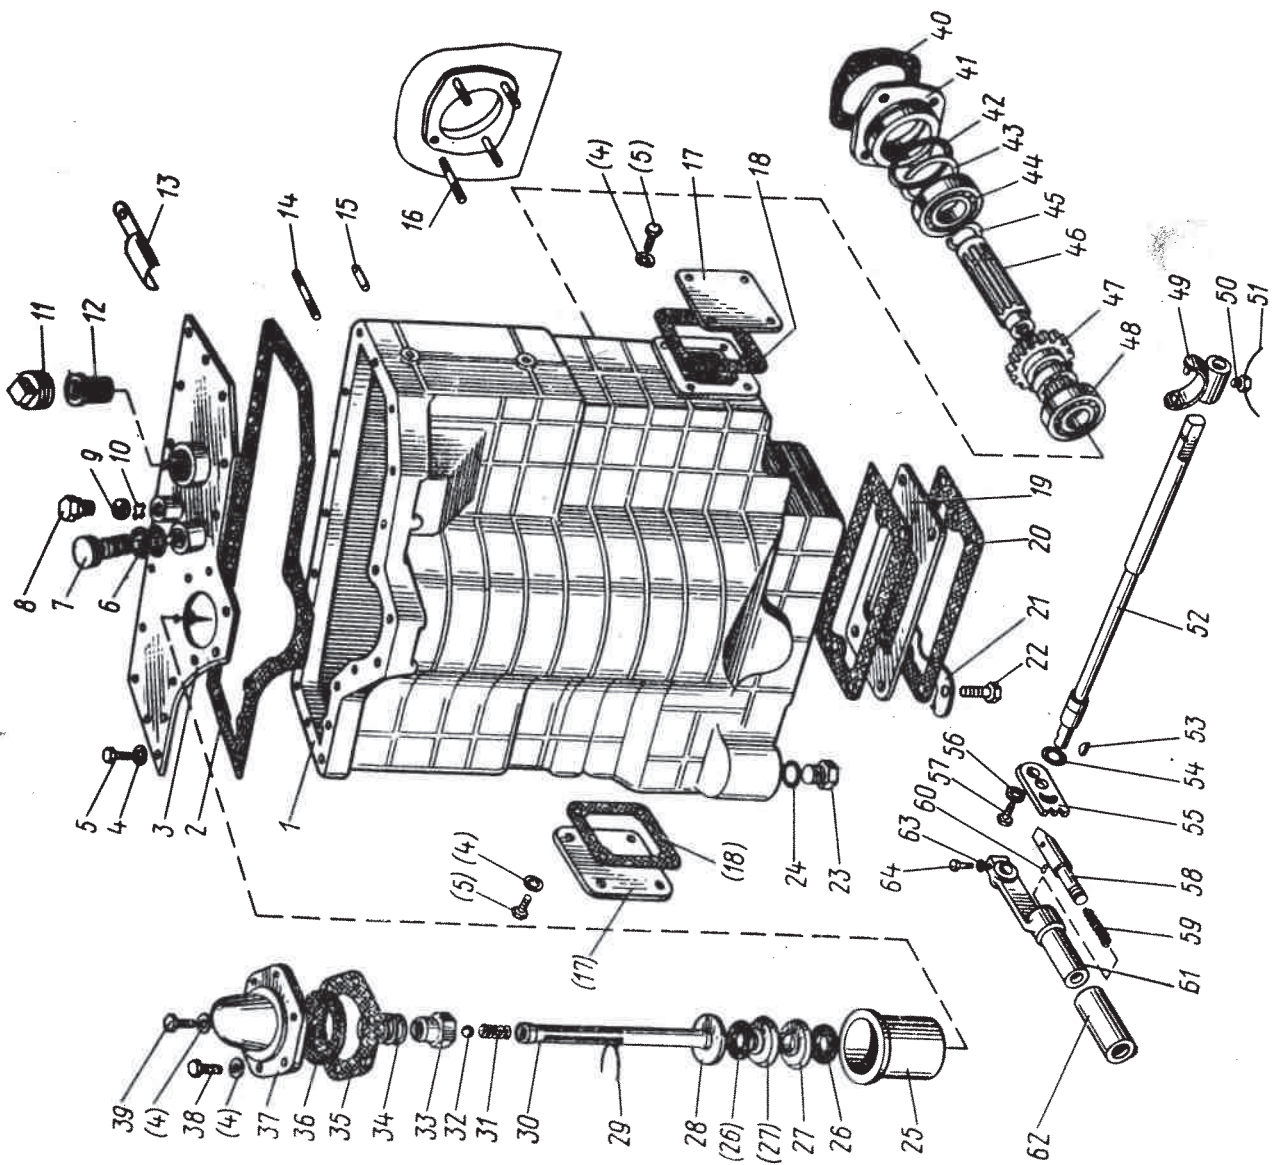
Корпус гидроагрегатов, фильтр и привод гидронасоса
